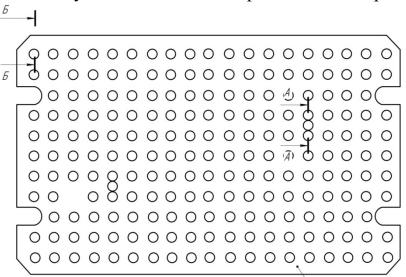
Плита с сеткой точно расположенных резьбовых отверстий
